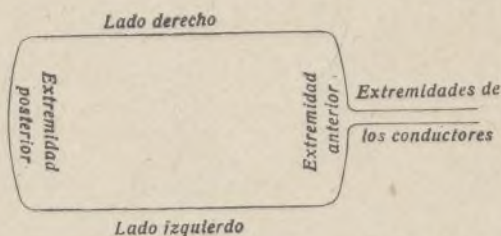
Nomenclatura de las partes de una bobina de devanado en tambor.
